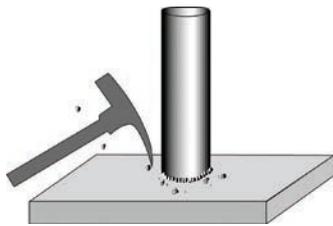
Résidus de flux de soudage retirés par burinage
